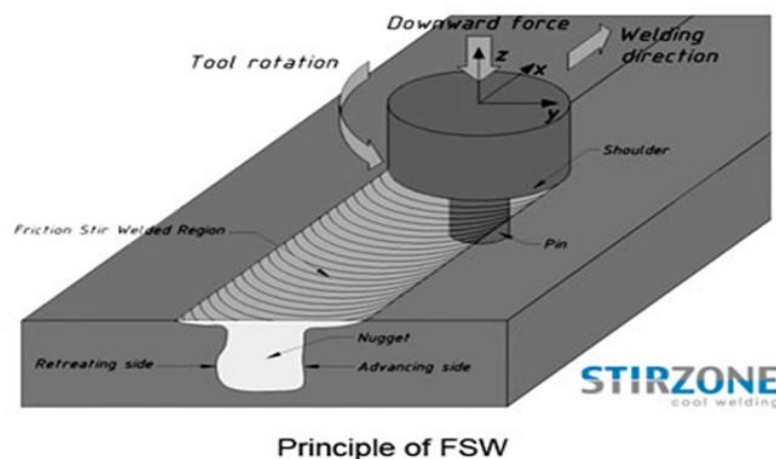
Prinsip *Frintion Stir Welding
